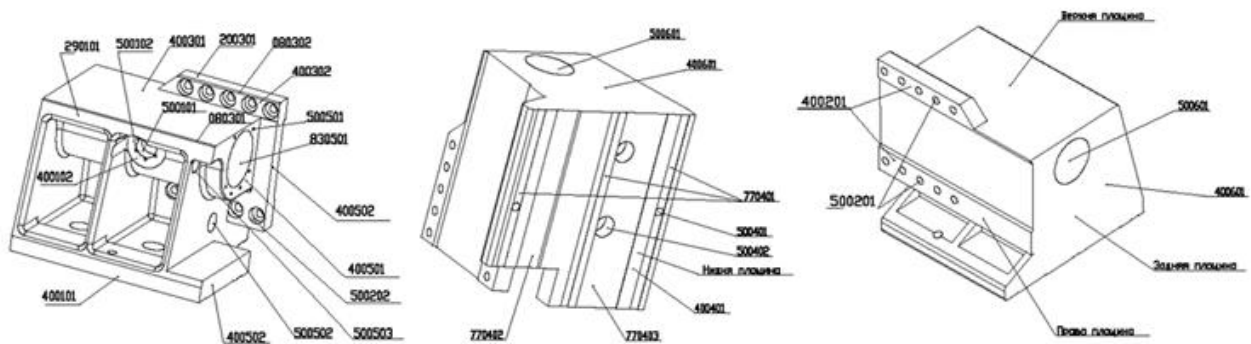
Кодування поверхонь деталі «Корпус центрової бабки»
